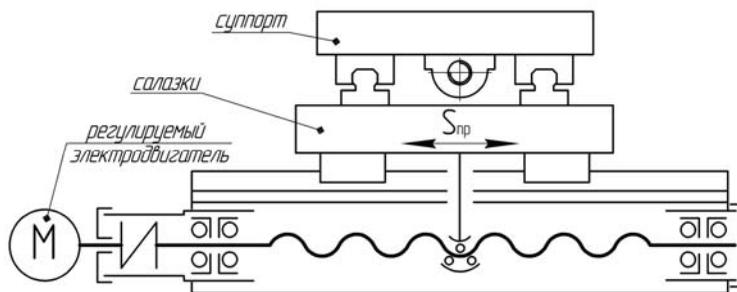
Структурно-кинематическая схема автономного привода с бесступенчатым регулированием продольной подачи суппорта  $s_{пр}$  без механического редуктора с прямым соединением вала электродвигателя и ходового винта токарного станка с ЧПУ
